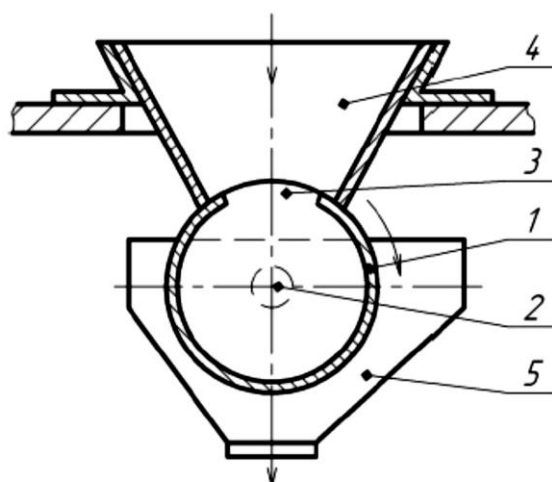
Конструктивна схема об'ємного дозатора
